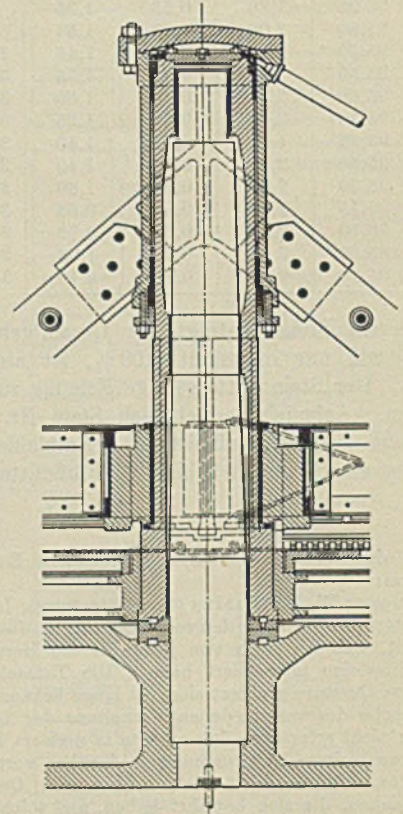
Hydraulische Hebevorrichtung für Gießwagen.
